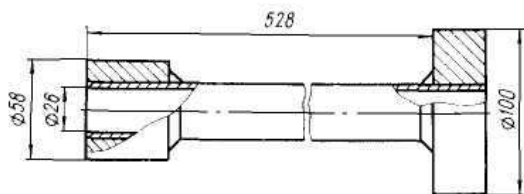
Подставка для запрессовки среднего подшипника с подушкой в сборе
